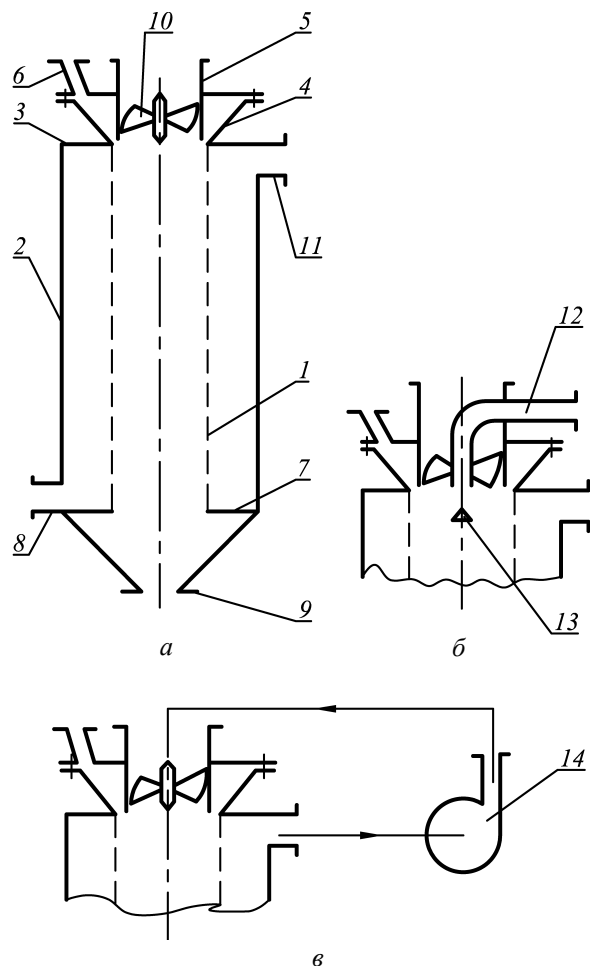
Газоцентрические фильтры: а – с пленочным вводом суспензии; б – с центробежным вводом суспензии; в – с замкнутым циклом по воздуху; 1 – проницаемый элемент; 2 – корпус; 3 – верхняя крышка; 4 – конический карман; 5 – патрубок подачи воздуха; 6 – штуцер подачи суспензии; 7 – нижняя крышка; 8 – патрубок отвода жидкой фазы; 9 – разгрузочное отверстие; 10 – лопаточный завихритель; 11 – патрубок отвода воздуха; 12 – питательная труба; 13 – конический отбойник; 14 – вентилятор
